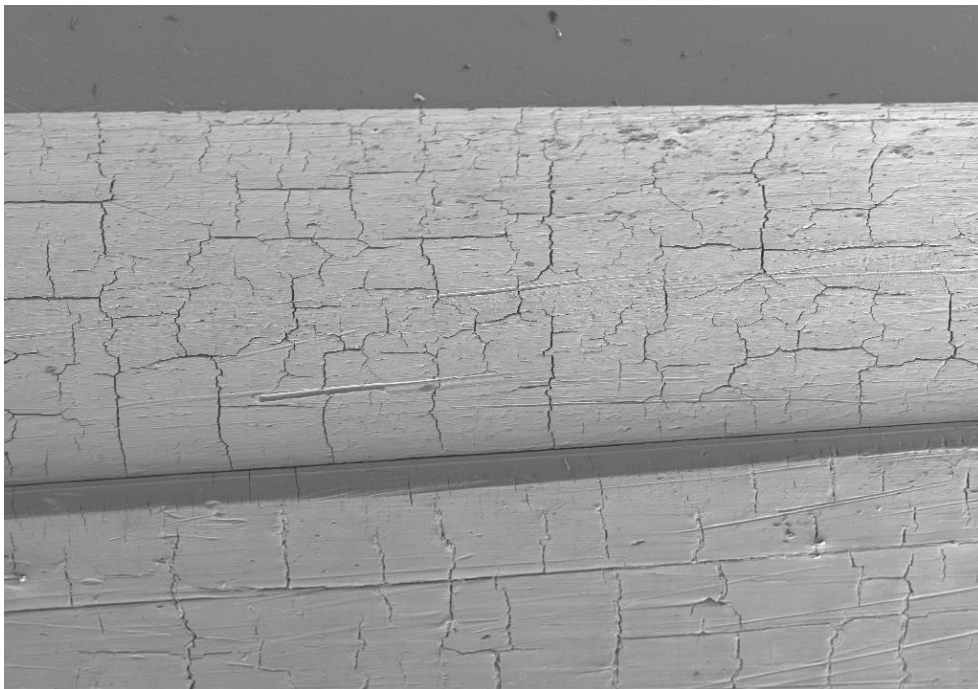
Detalle de las grietas en la región de la boca del ánima, donde se aprecian los surcos paralelos a la dirección de movimiento del proyectil.
